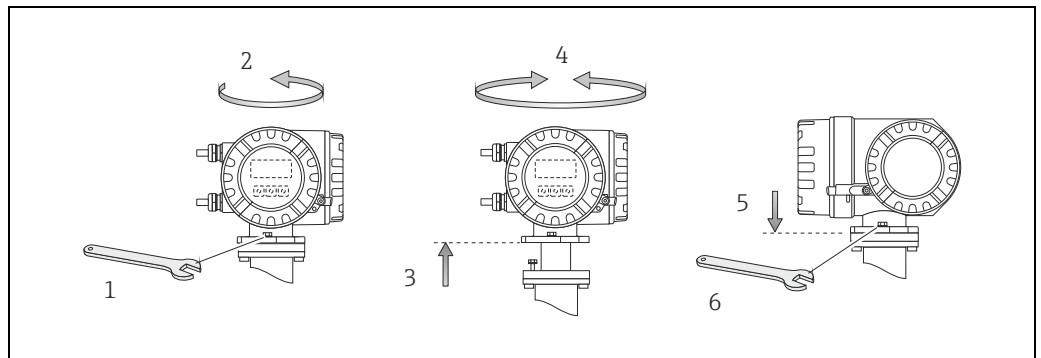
Drehen des Messumformergehäuses (Aluminium-Feldgehäuse)
